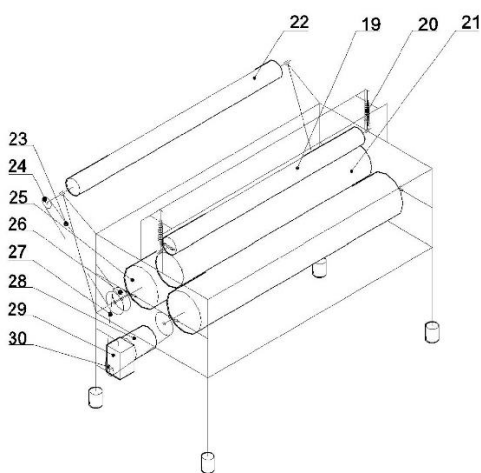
Кинематическая схема сматывающего устройства: 19 – прижимной валик; 20 – пружина; 21 – рулон материала; 22 – валик обеспечения компенсационной петли; 23 – цепная передача петли
